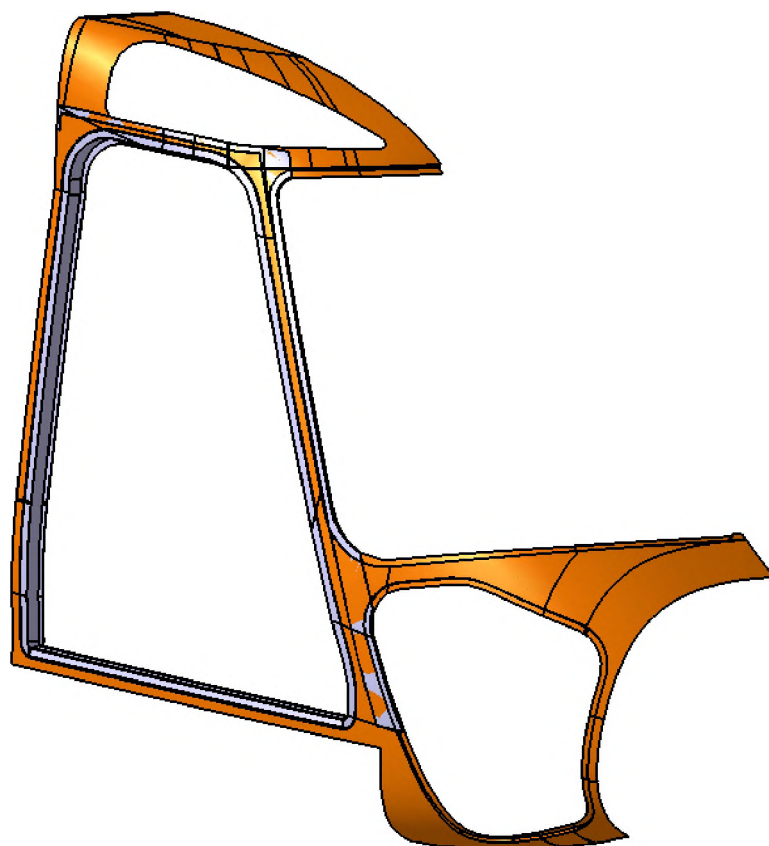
Заготовка фонаря кабины экипажа из углепластика вертолета Ка-226А.
